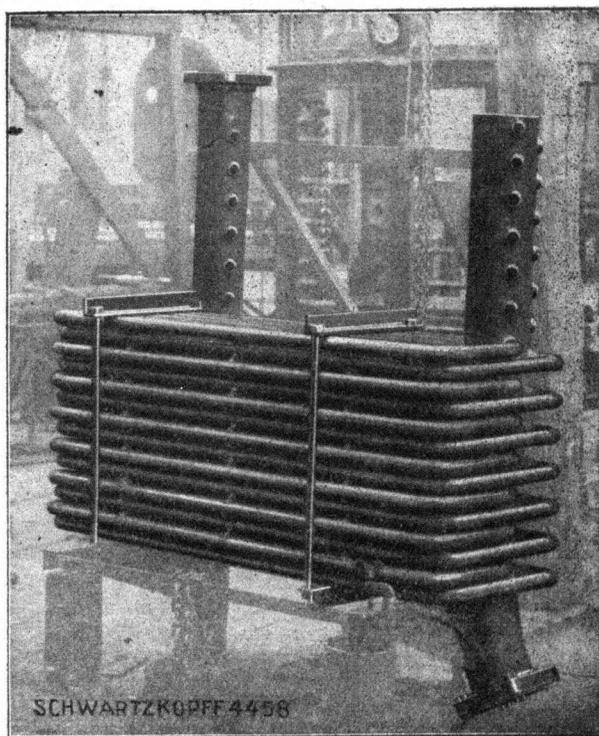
Niederdruck-Ueberhitzer in Bearbeitung.
